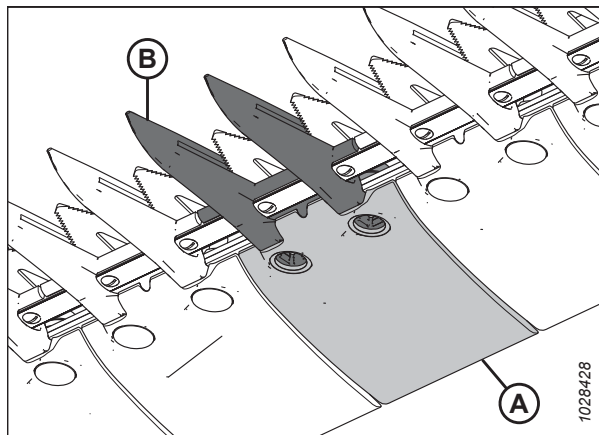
Заостренный противорежущий палец и износная пластина
